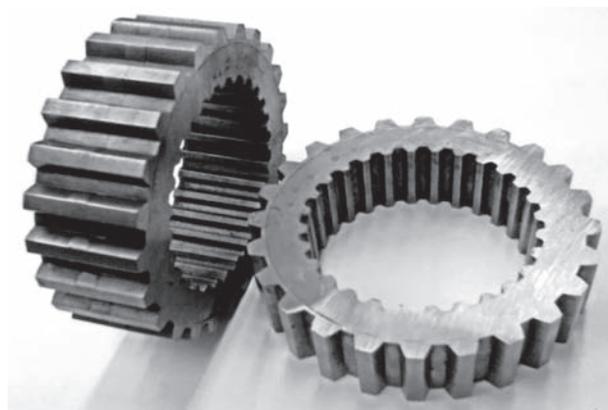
Втулки 75-1701352, изготовленные методом порошковой металлургии
